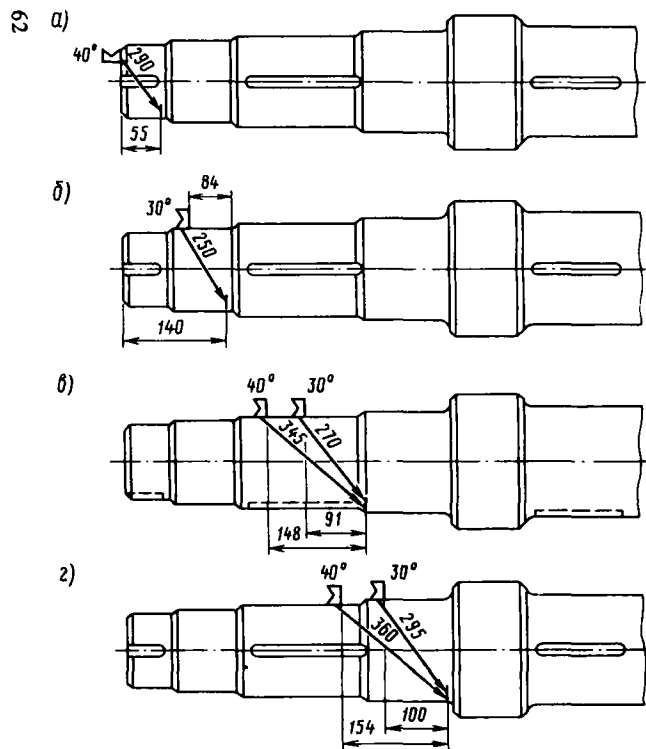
Схемы и зоны контроля наклонными искателями главного приводного вала эскалатора ЛП-7К в разных его сечениях (а, б, в, г) с левого торца вала
